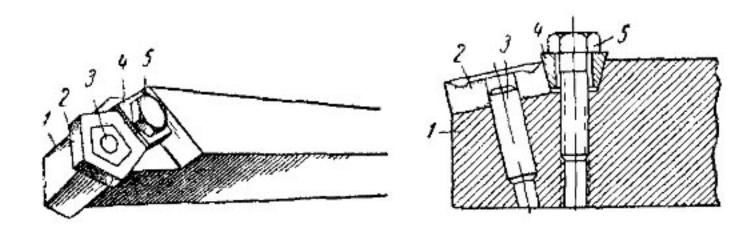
Резец с неперетачиваемой многогранной твердосплавной пластинкой конструкции ВНИИИ
